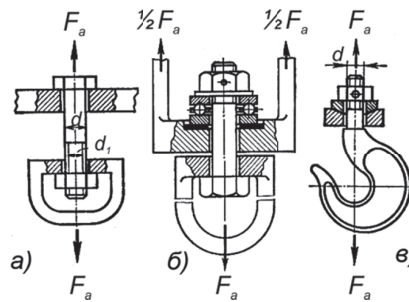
Резьбовые соединения без предварительного напряжения затяжки
